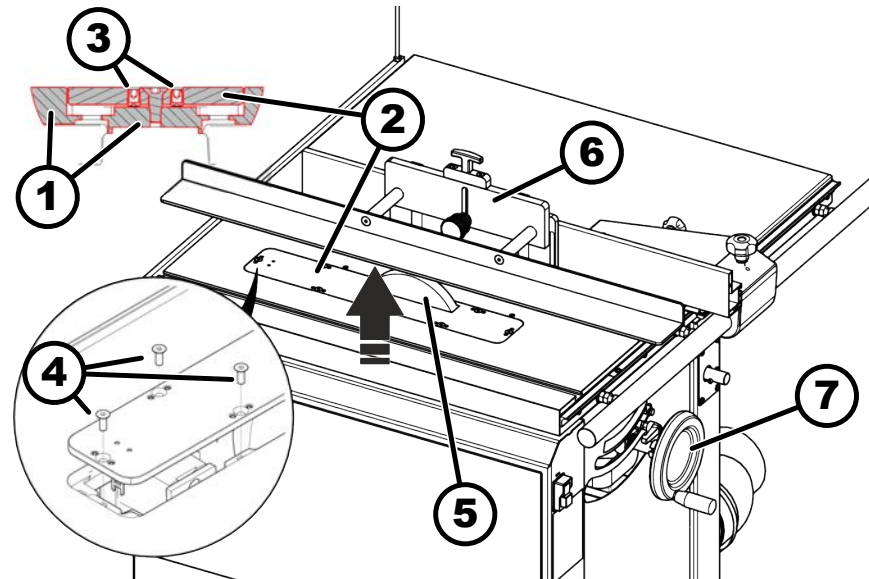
Einlegebrett für Nutwerkzeuge einbauen
